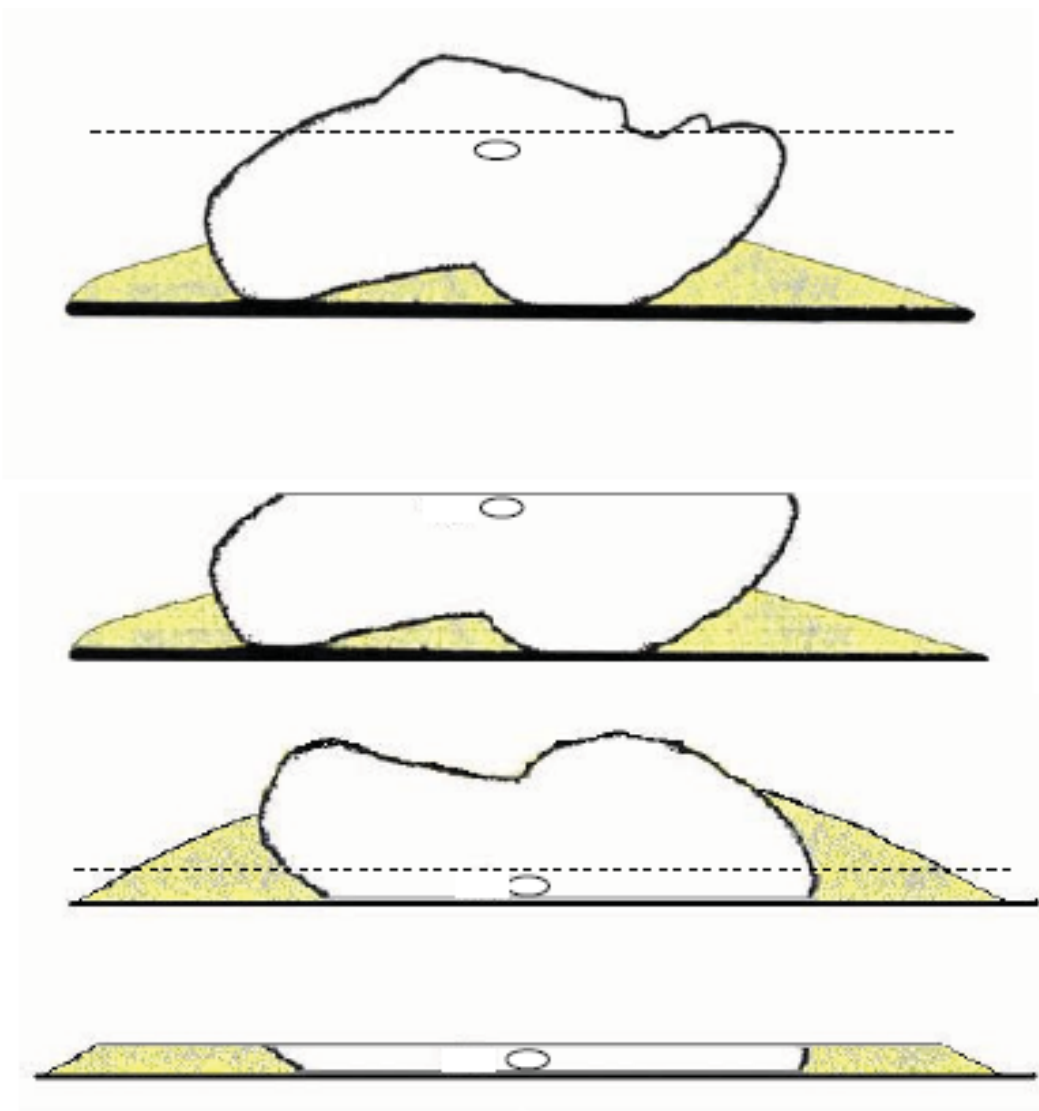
Lavorazione della faccia opposta (vista in sezione)
